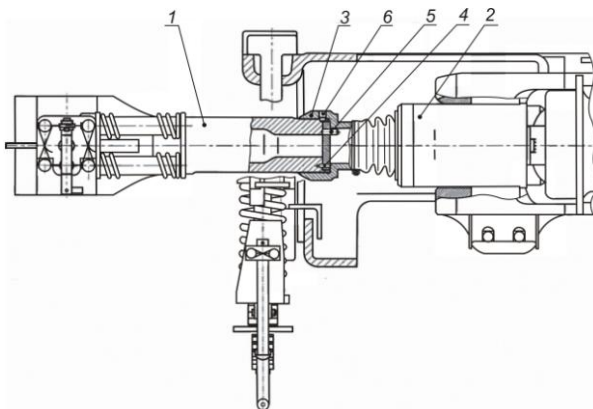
Сцепное устройство БСУ-3 с монолитным корпусом (вид сбоку):
